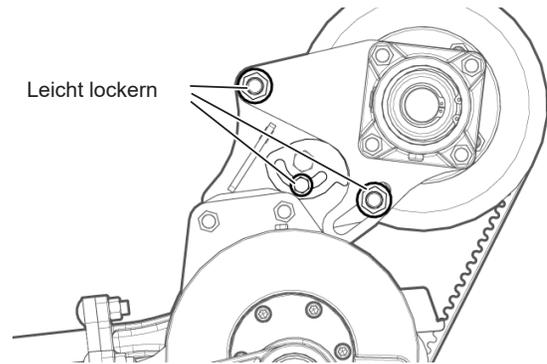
Spannung des Messerriemens – Sicherungsmuttern und Schrauben lösen
